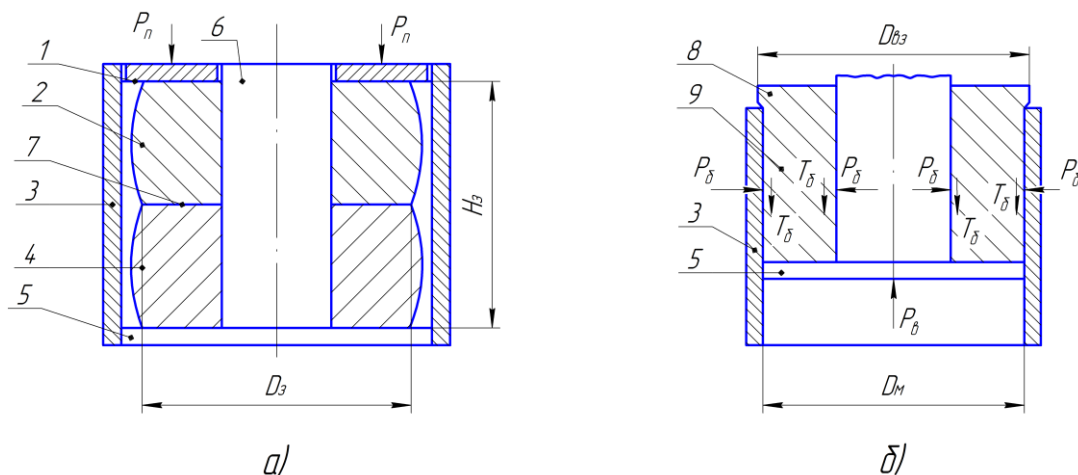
Схема прессования (а) и выталкивания заготовки (б)
